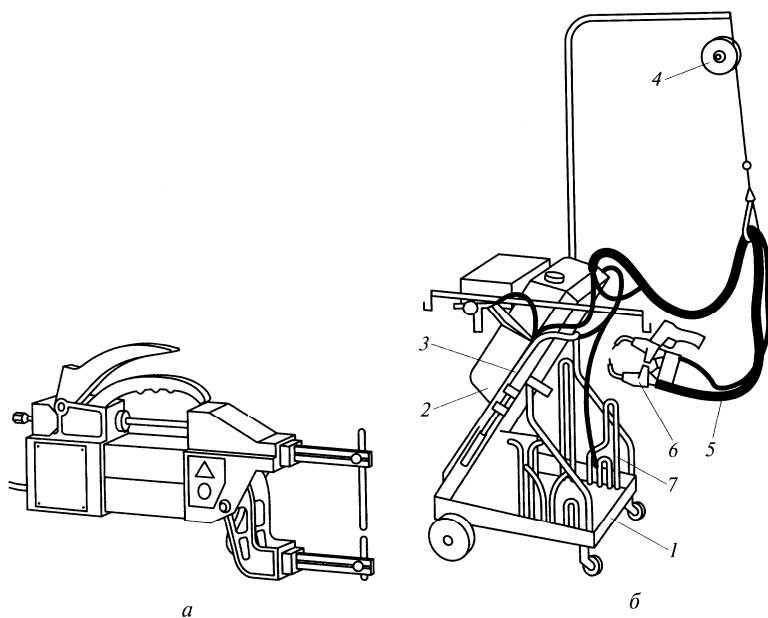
Ручные сварочные клещи (а) и универсальный аппарат контактной сварки (б): 1 – тележка; 2 – внешний источник тока; 3 – споттер; 4 – балансир; 5 – гибкий кабель; 6 – сварочные клещи; 7 – сменные электроды
